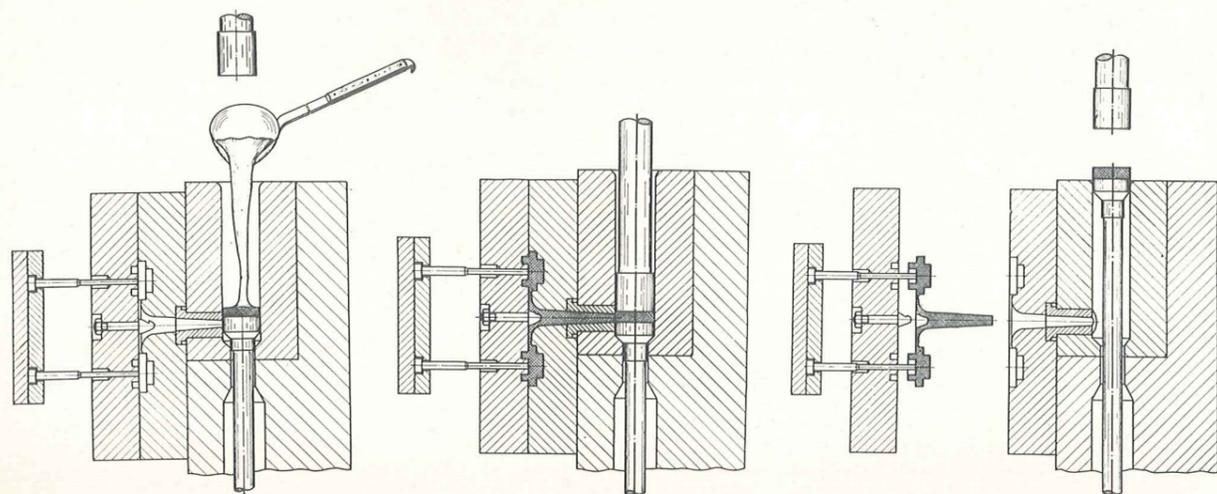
Füllzylinder mit Druckkolben beim Eingießen des Metalles einer Druckgußmaschine mit senkrechter Druckkammer und geschlossener Form
